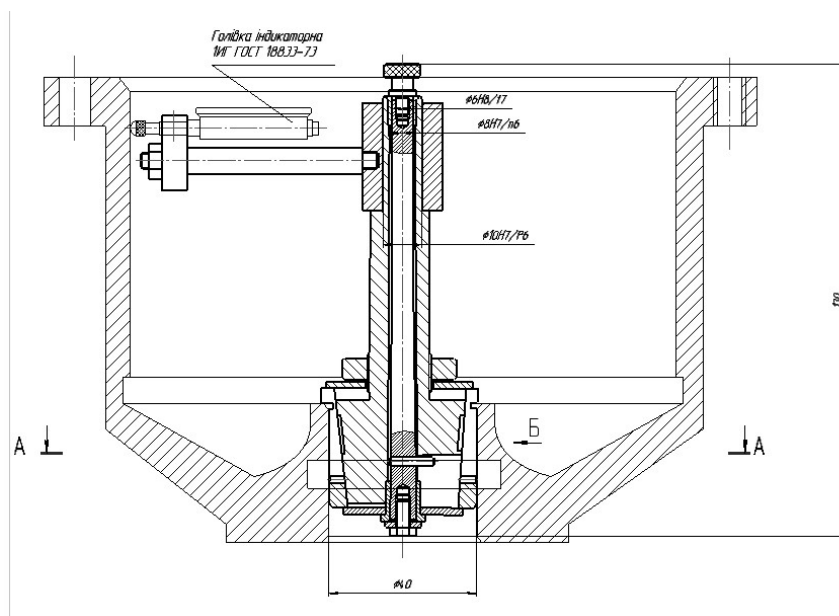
Схема роботи пристрою при вимірюванні
